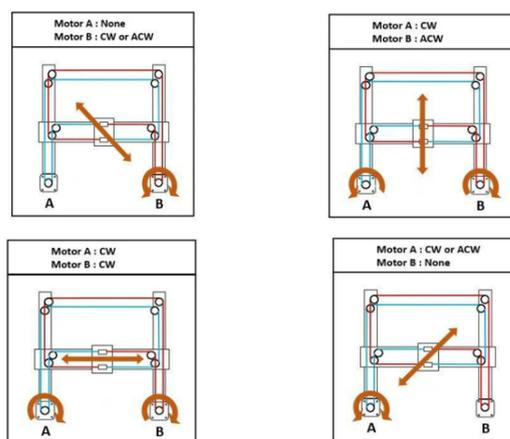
Movimentações da plataforma central consoante à direção do motor no mecanismo CoreXY.
